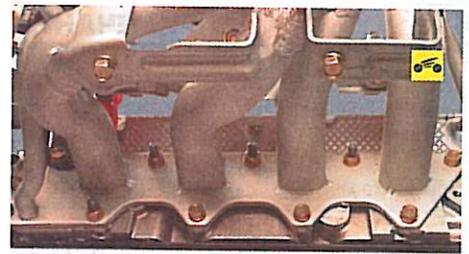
Головка блока цилиндров двигателя SOHC, снятая с автомобиля (вид сбоку): 1 – зубчатый шкив распределительного вала; 2, 7 – транспортные проушины; 3 – ось коромысел клапанов; 4 – впускная труба; 5 – коромысло клапанов; 6 – поддерживающий кронштейн впускной трубы
